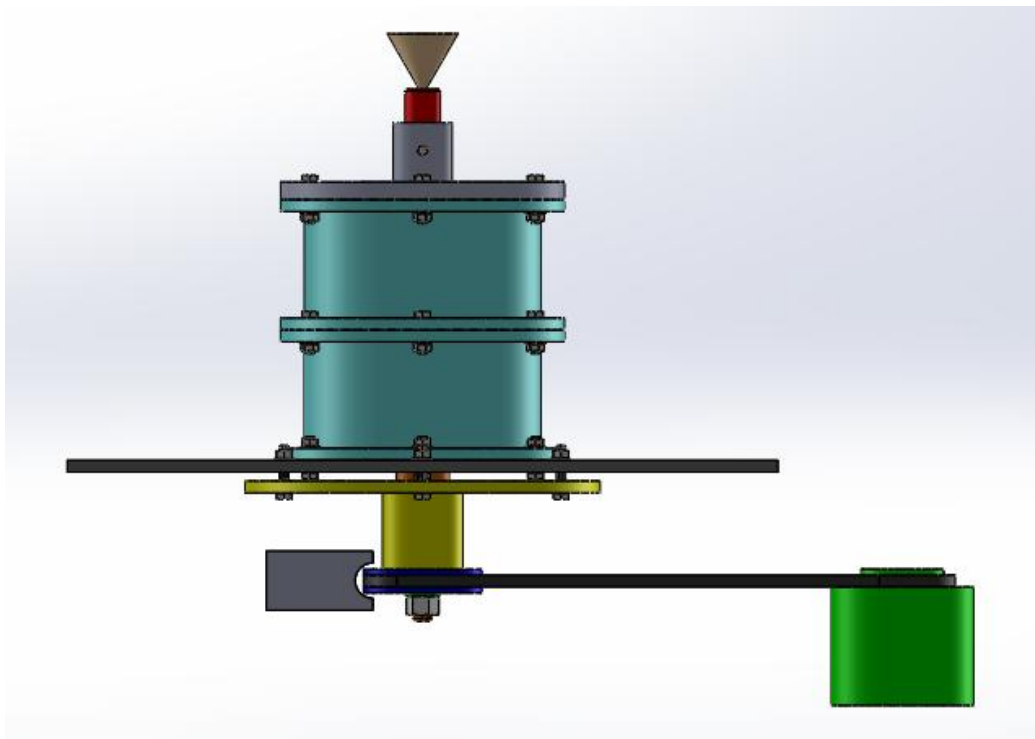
Vue de face de la partie fixe et mobile du réacteur de mécanofusion.
